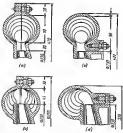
Verlantes de la construcción de las volutas de salida La construcción de tai voluta espirel con separección en el plano
